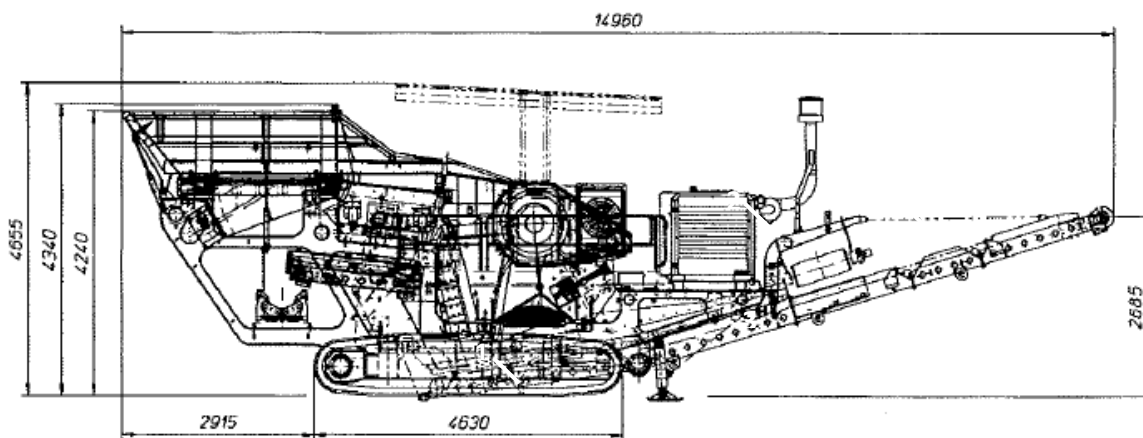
Dimensioni del frantoio mobile REV GCR 106
